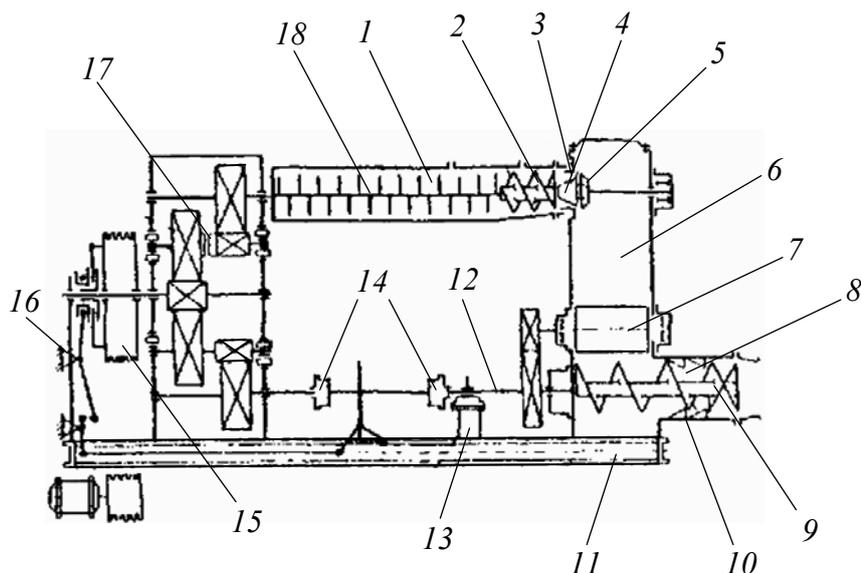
Кинематическая схема ленточного вакуум-пресса СМК-443А:
